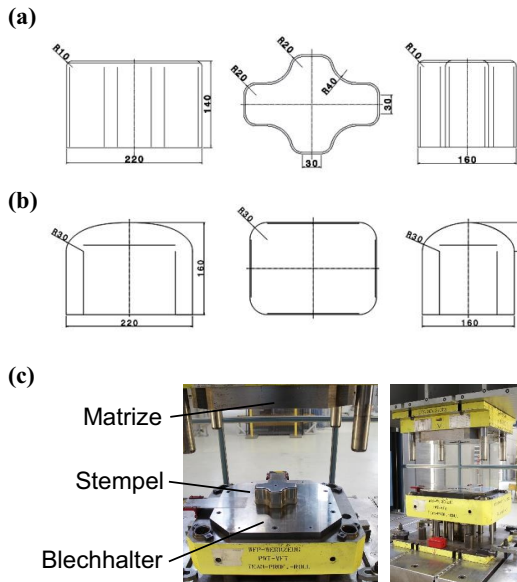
(a) Kreuzstempel; (b) Bombierter Stempel; (c) Werkzeug
